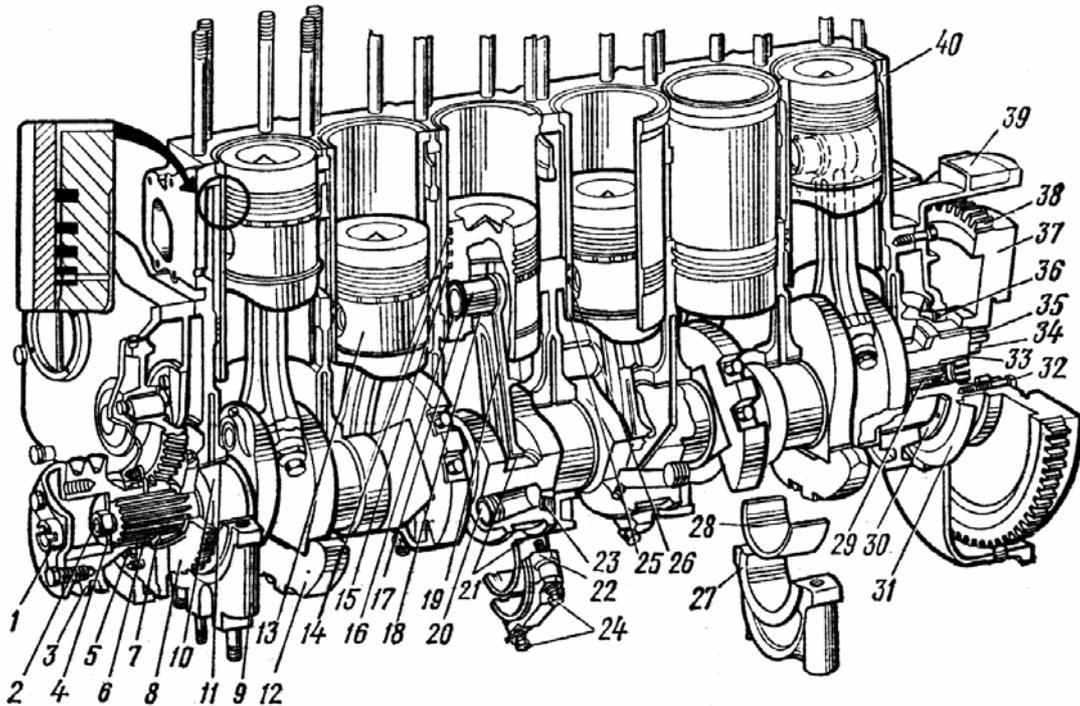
Кривошипно-шатунный механизм двигателя А-01М:
